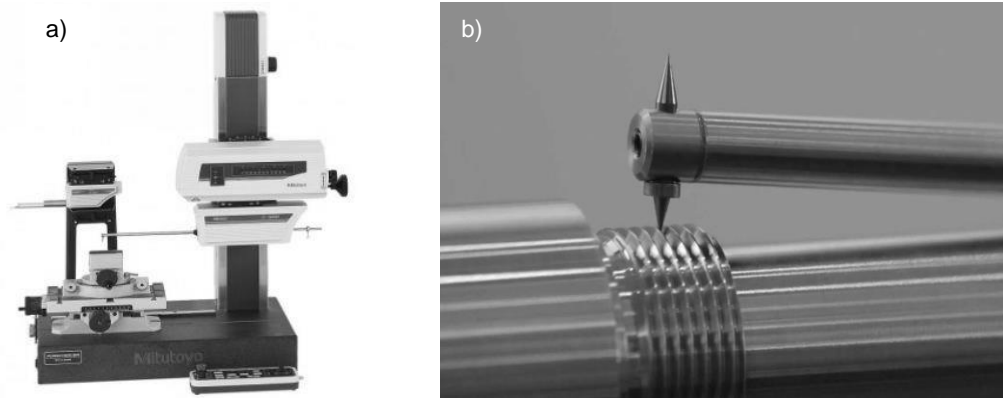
Equipo para medir rugosidad superficial; a) Rugosímetro, equipo que caracteriza superficies y b) Palpador del rugosímetro [110].
